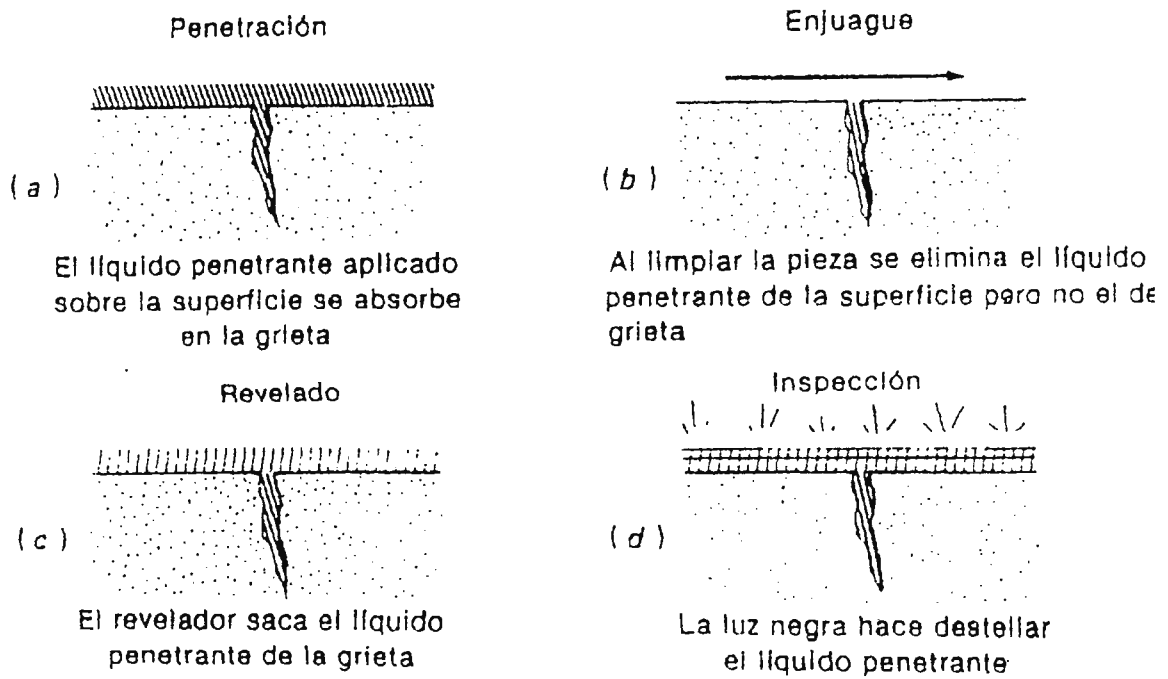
Forma de aplicar líquido penetrante en cordón de soldadura .
